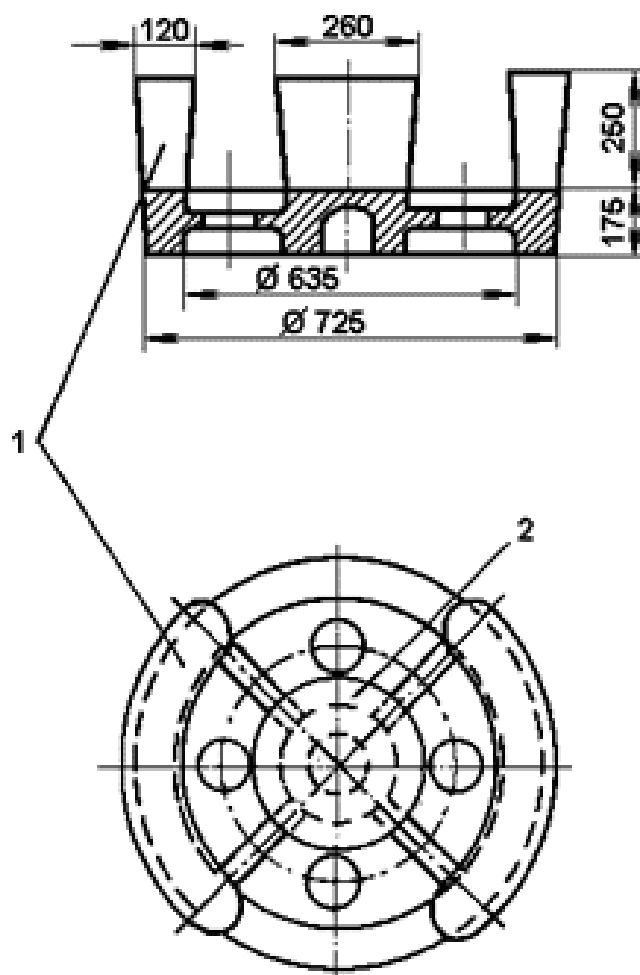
Установка прибылей на отливке «Зубчатое колесо»:
